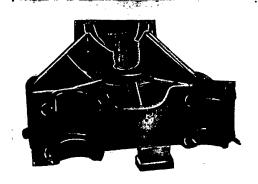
Kümpelpressen-Tischhälfte von 4000 kg Gewicht mit ausgebrochener Halterung für den Preßzylinder. Wandstärke an der Bruchstelle 40 mm.
